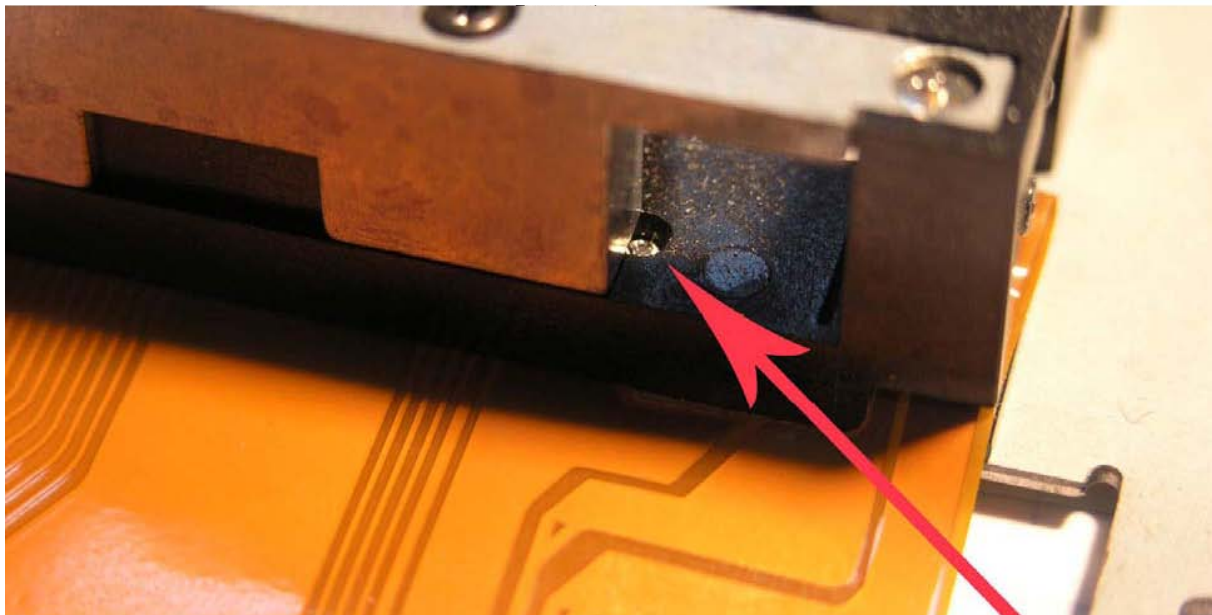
Короткий саморез не обеспечивает контакт (головка для наглядности демонтирована из корпуса)
